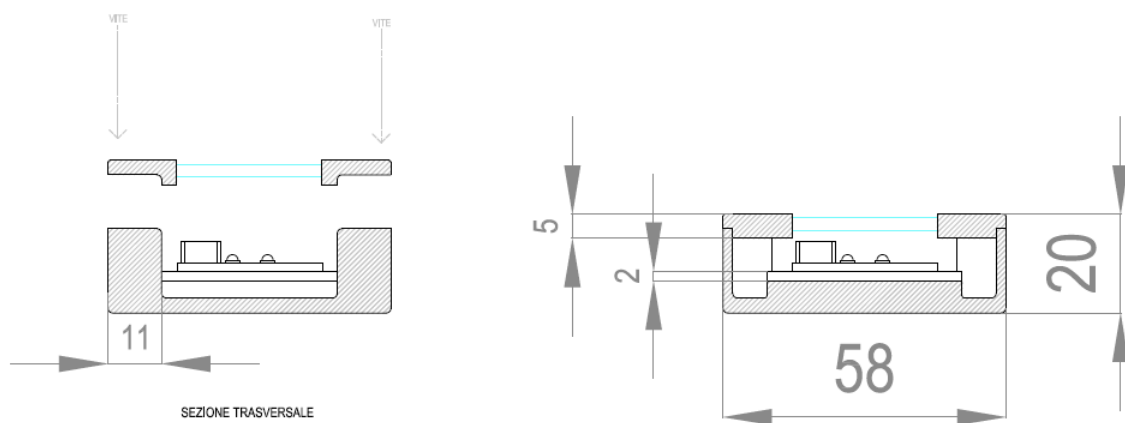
Vista in sezione trasversale del modulo applique a parete
